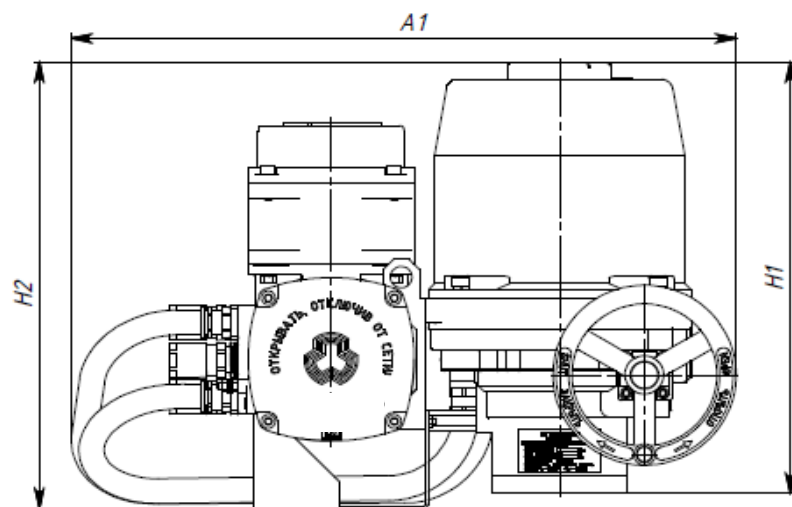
к – Габаритные размеры привода конструктивной схемы 2 с блоком управления ВЭЗ
